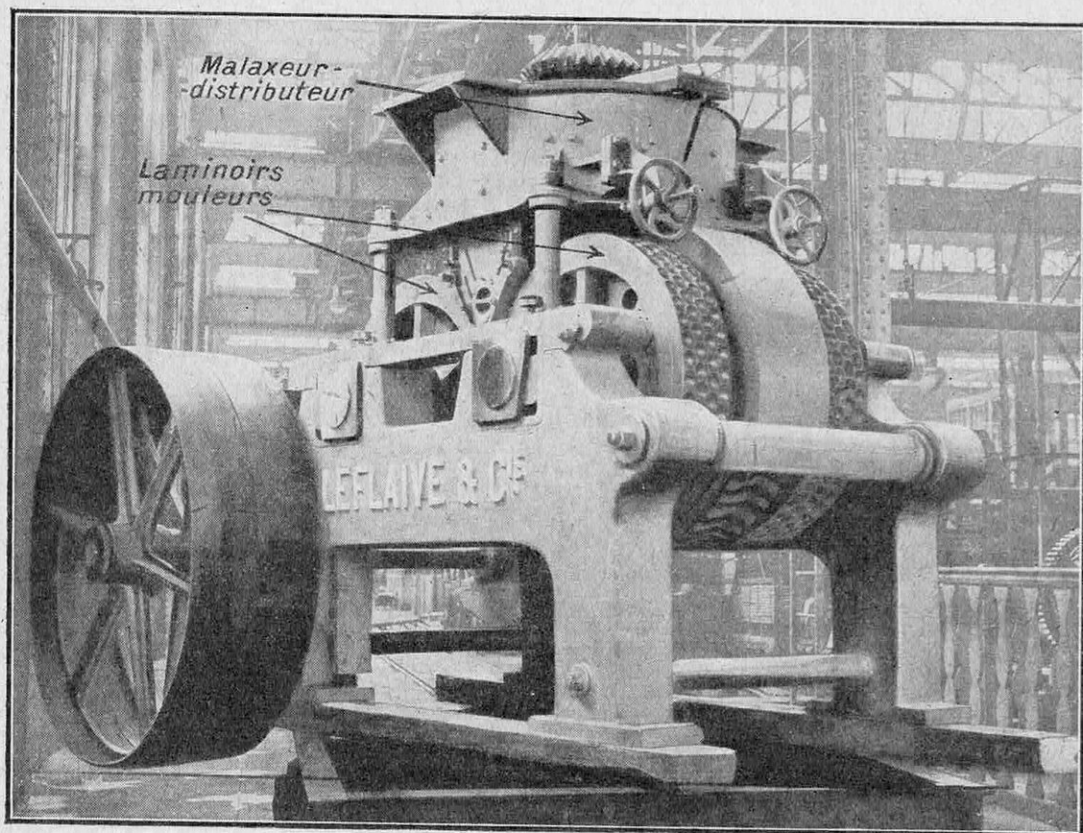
ENSEMBLE D'UNE PRESSE A BOULETS
